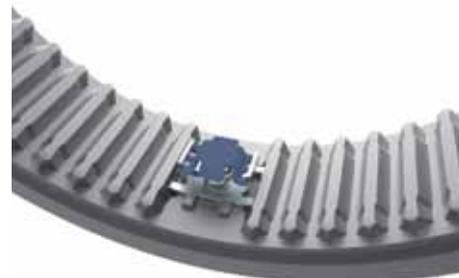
Schiebemuffe mit integrierter Arretierung (Strut-in-Sleeve)
